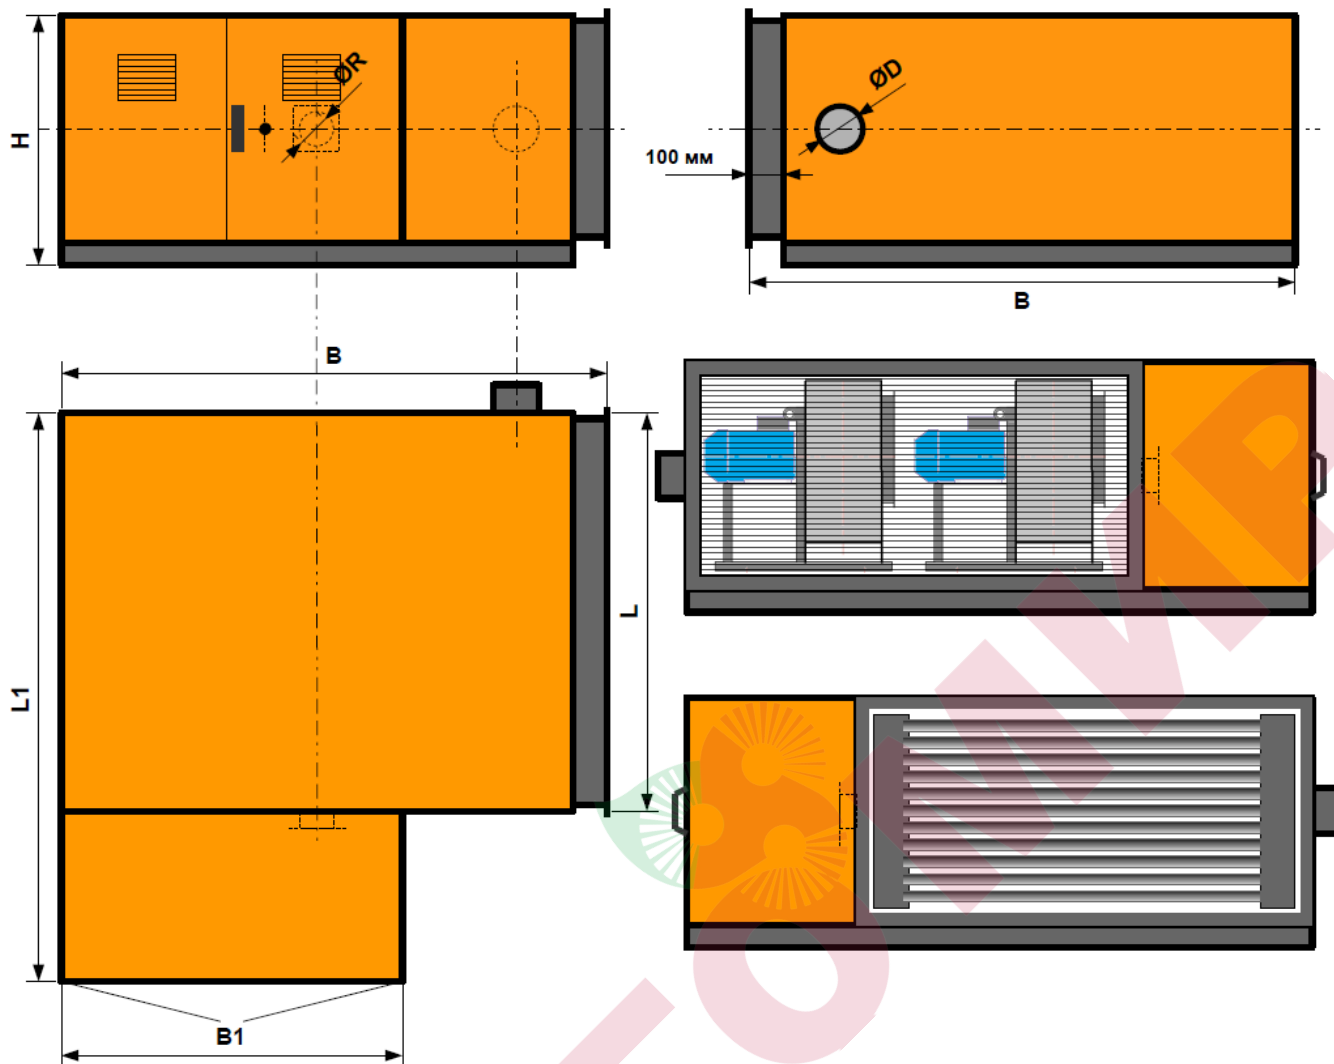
Габаритные размеры воздухонагревателей серии НТ-О
